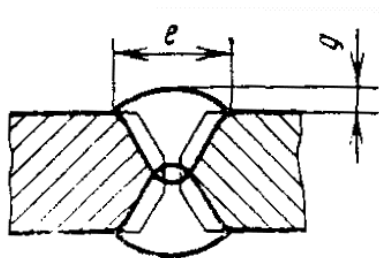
Размеры сварного соединения:  $e=10\pm 2$  мм,  $g=1\pm 1$  мм
